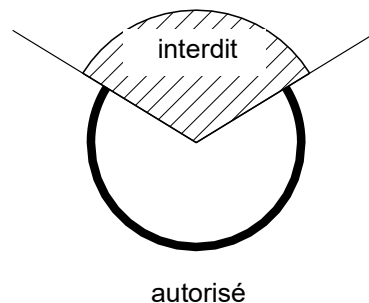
Position du joint de soudure de la chambre de combustion
